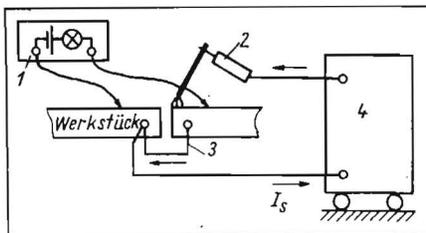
Anschluß der Schweißstromquelle und des Durchgangsprüfers beim Elektroschweißen in belegten Tieranlagen; 1 Durchgangsprüfer zur Kontrolle vor dem Schweißen, 2 Elektrodenhalter, 3 Kabelbrücke, 4 Schweißstromquelle
